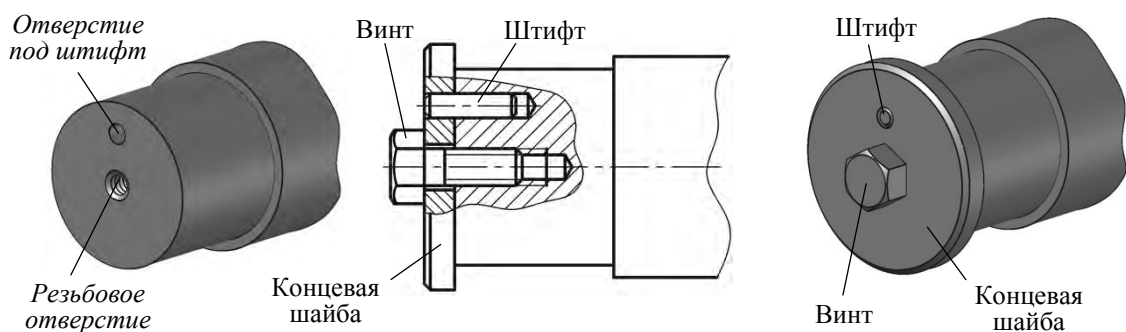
Крепление концевой шайбы на торце вала посредством винта и стопорного штифта (посередине – чертеж соединения)
